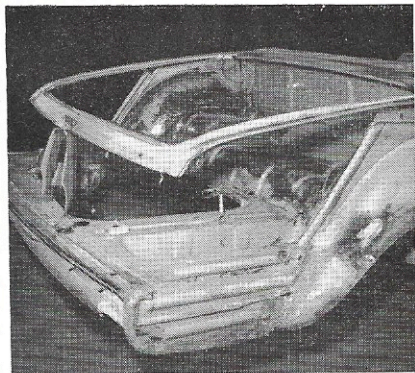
Vue arrière du cabriolet, revêtement et couvercle de coffre déposés.
